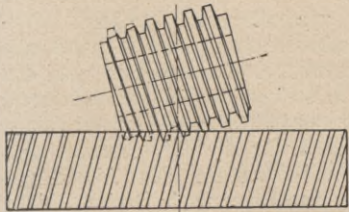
Abgeschrägter Fräser zum Bearbeiten stark geneigter Schraubenräder
